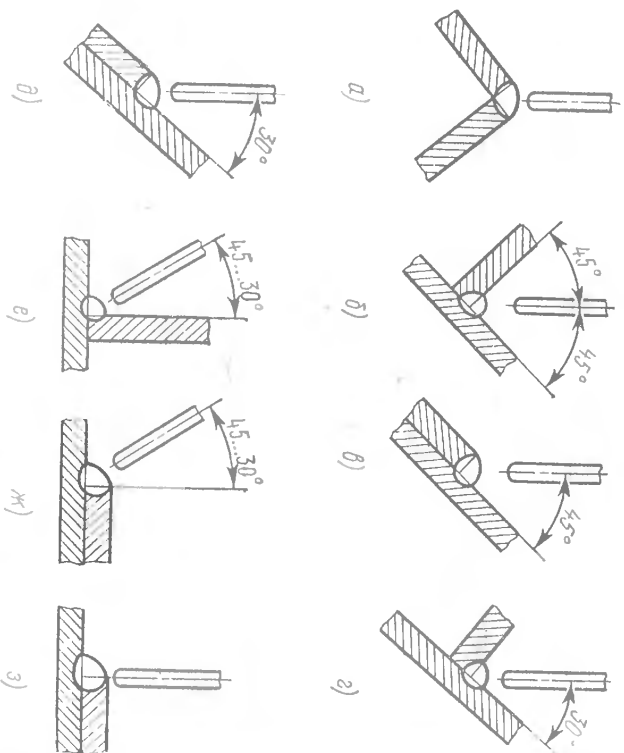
Способы выполнения угловых, тавровых и нахлесточных сварных соединений:
